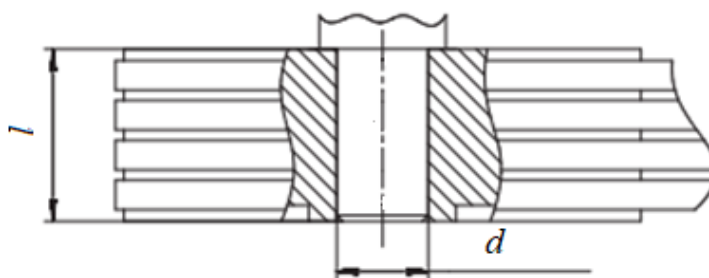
Установка шкива клиноременной передачи на валу двигателя
